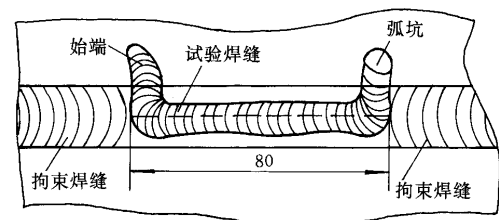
采用手工电弧焊时试验焊缝的位置
